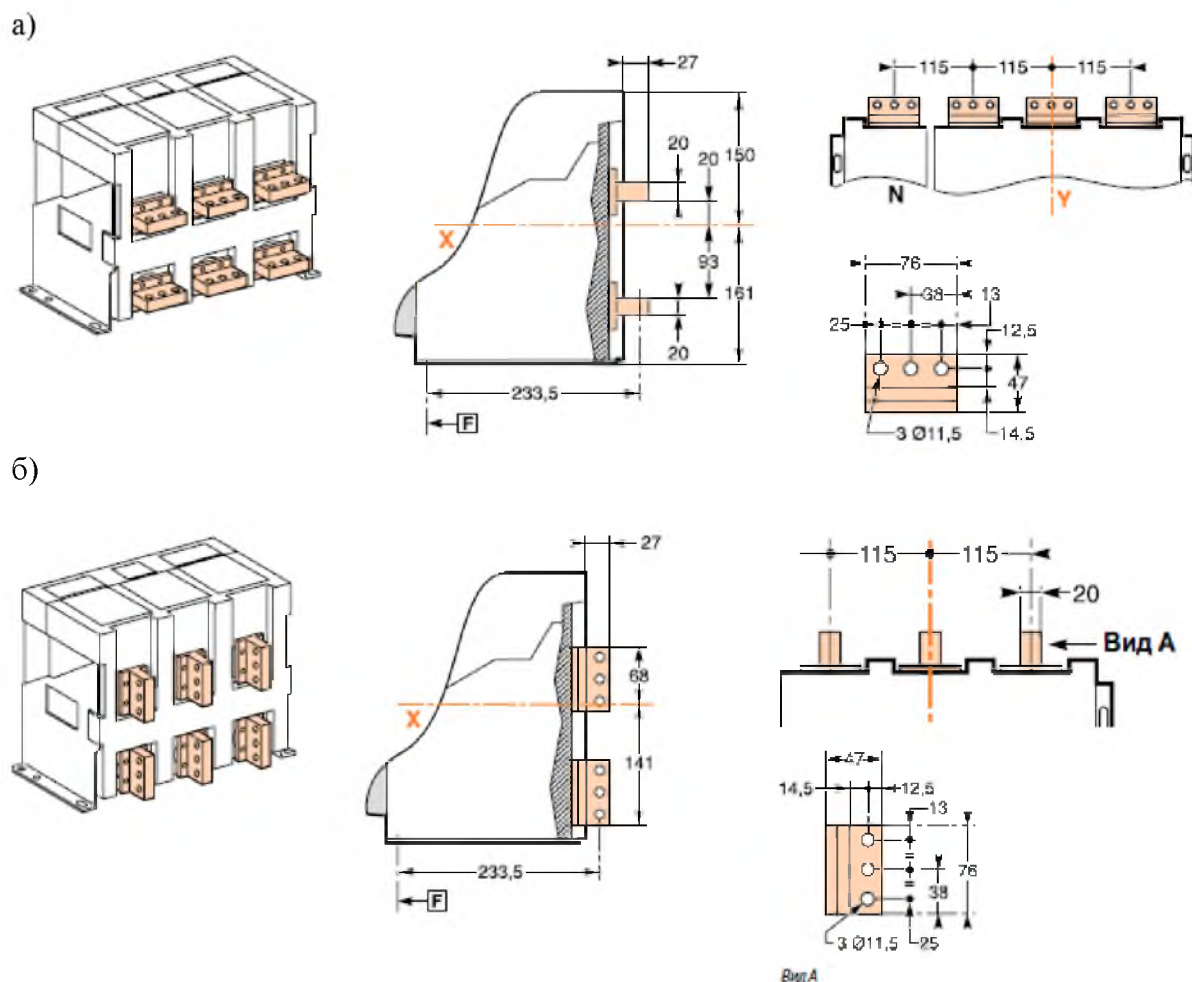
Горизонтальные и вертикальные выводы для заднего присоединения с присоединительными размерами для ВА–СЭЩ–АС08/10/12/16/20/25/32 стационарного исполнения
